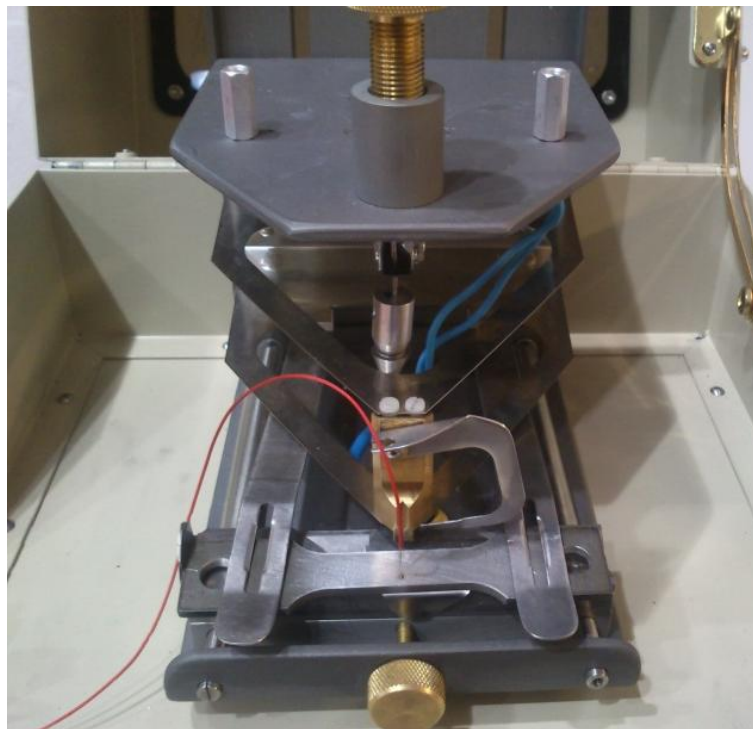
Anschweißen der Thermoelemente auf die Gleeble-Probe am Kondensatorentladungsschweißgerät.
